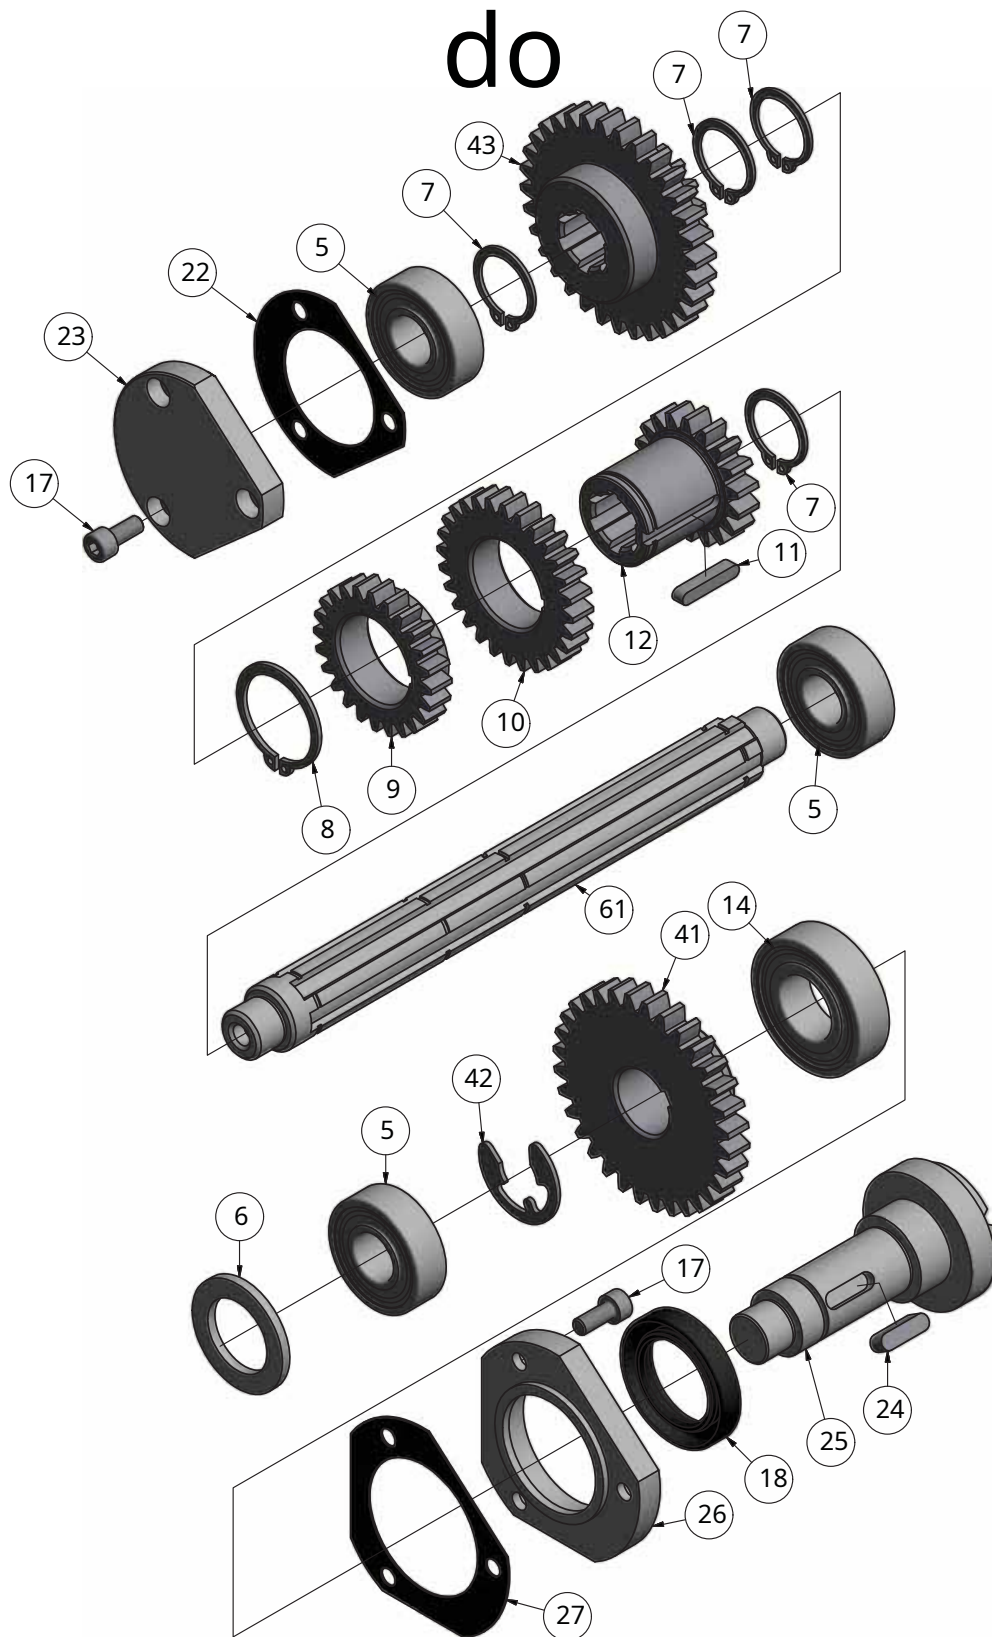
Vorschubgetriebe 5-6 - Engranaje de alimentación 5-6
